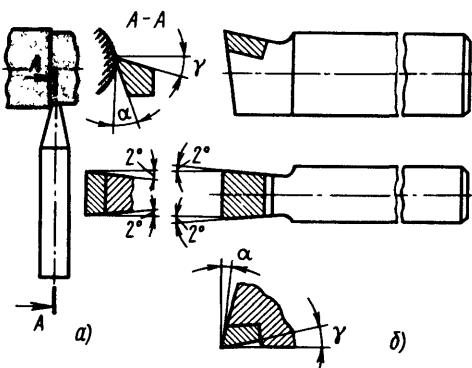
Чистовой резец для точения с малой подачей (а) и чистовой лопаточный резец для точения с большой подачей (б)
